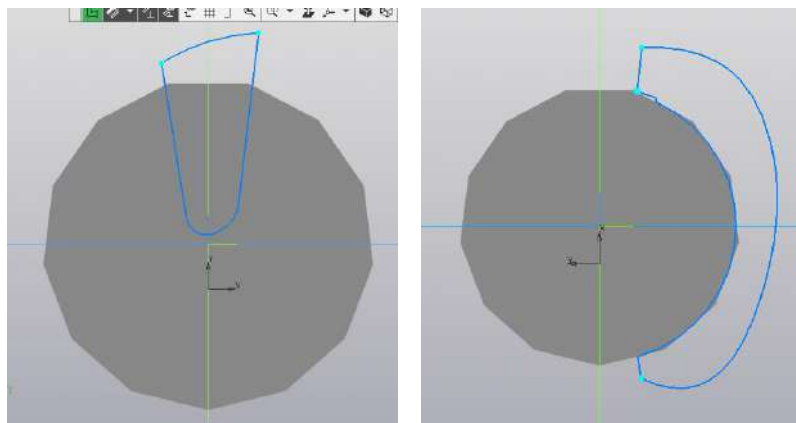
Эскиз стружечной канавки и ленточки на сверле
